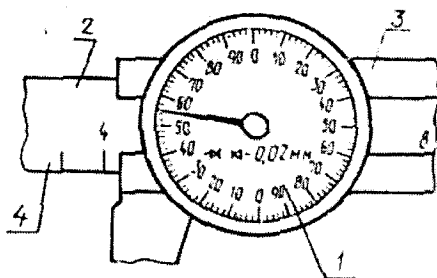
Штангенциркуль з коловою шкалою відлікового пристрою:
